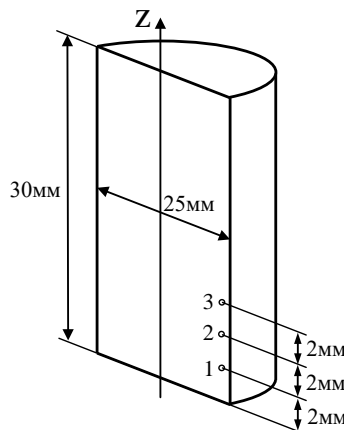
Розташування точок 1, 2, 3 на меридіональному перерізі заготовки
